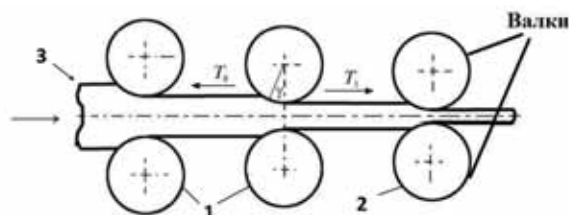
Условная схема формирования профиля арматурного проката, формирование сечения профиля арматуры валками прокатных клетей
